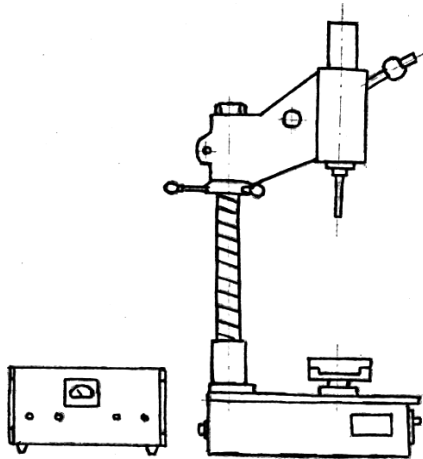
Внешний вид установки оплавления термопластичных материалов
